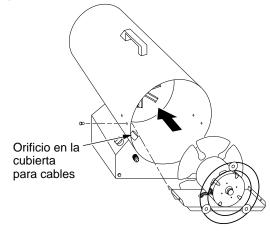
Reemplazo del motor, del montaje del motor y del resguardo del ventilador en el calentador
